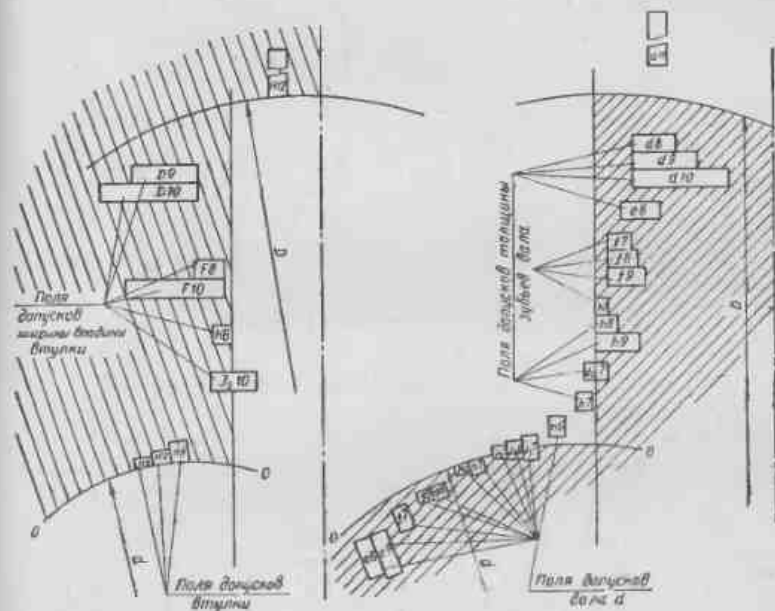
Схема расположения полей допусков шлицевых соединений с прямым профилем
